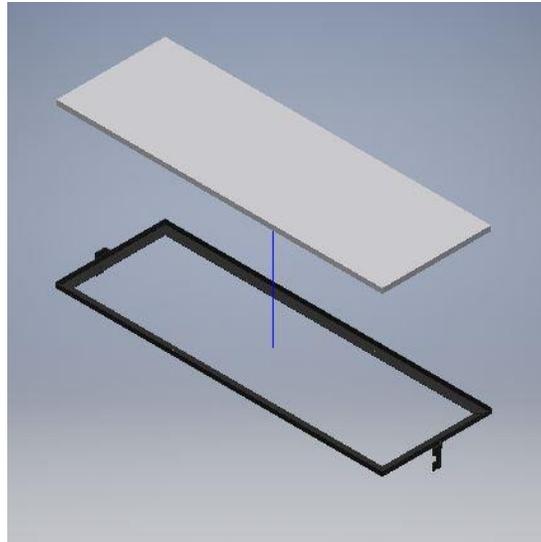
Explosionado de la balda del Pop Up
